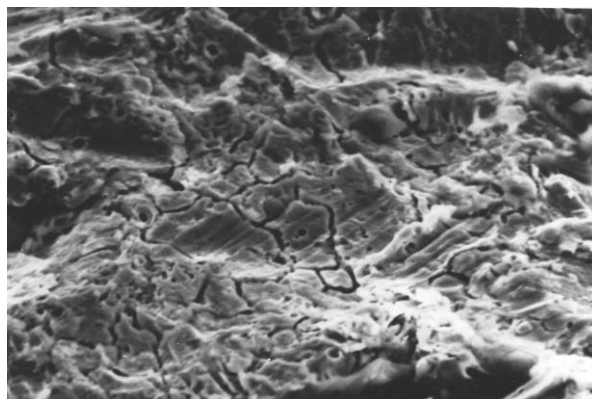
Микротрещины на поверхности резьбы оси-болта из стали 95X18, x 3200
